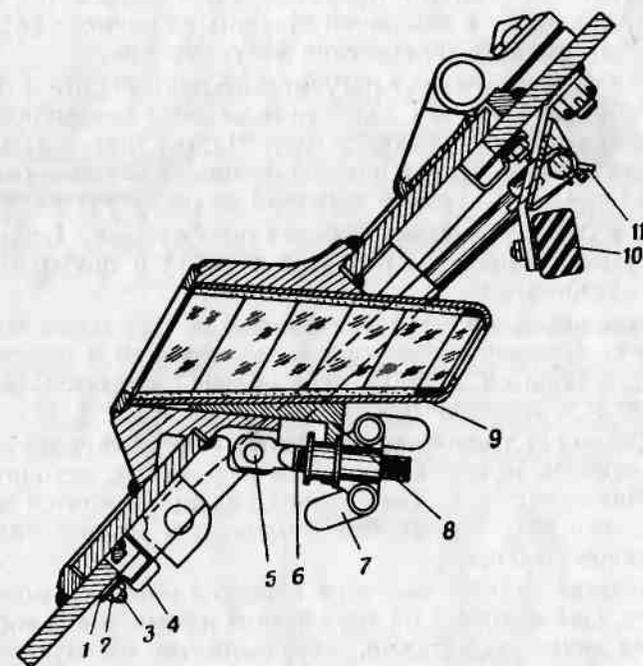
Крышка люка лобового листа с прибором наблюдения в закрытом (боевом) положении:
